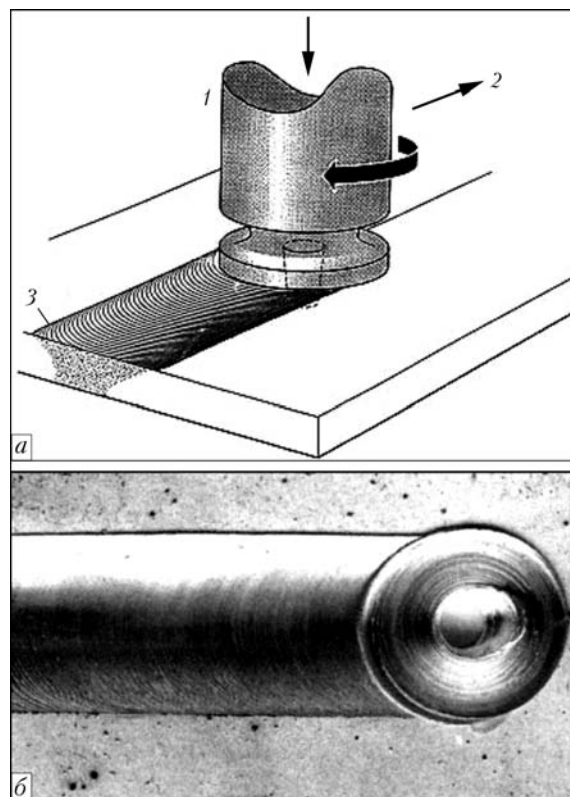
Схема процесса сварки трением с перемешиванием нанодисперсного алюмокомпозита Al+7 % Al_2O_3 (а) и внешний вид шва (б): 1 — вращаемый рабочий инструмент; 2 — направление перемещения инструмента при сварке; 3 — шов
